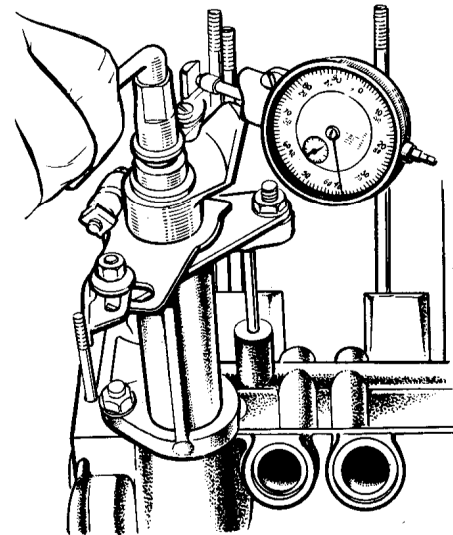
Проверка бокового зазора в зацеплении шестерни привода распределителя при помощи приспособления с индикатором
